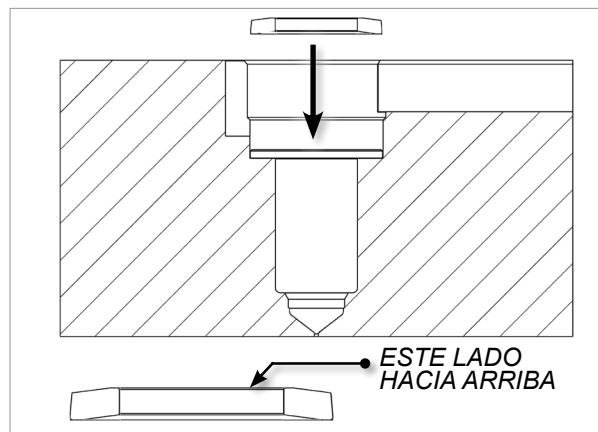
Boquilla y componentes de ThinPAK y MasterSHIELD
